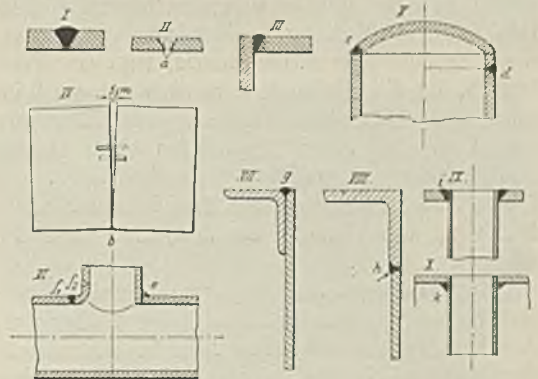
Beispiele autogener Schweißungen.
